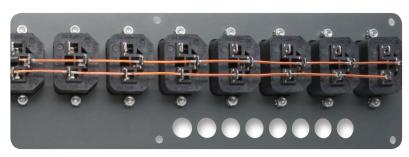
Die N- und PE-Anschlüsse der Kaltgerätebuchsen sind mit Draht durchzuverbinden.
